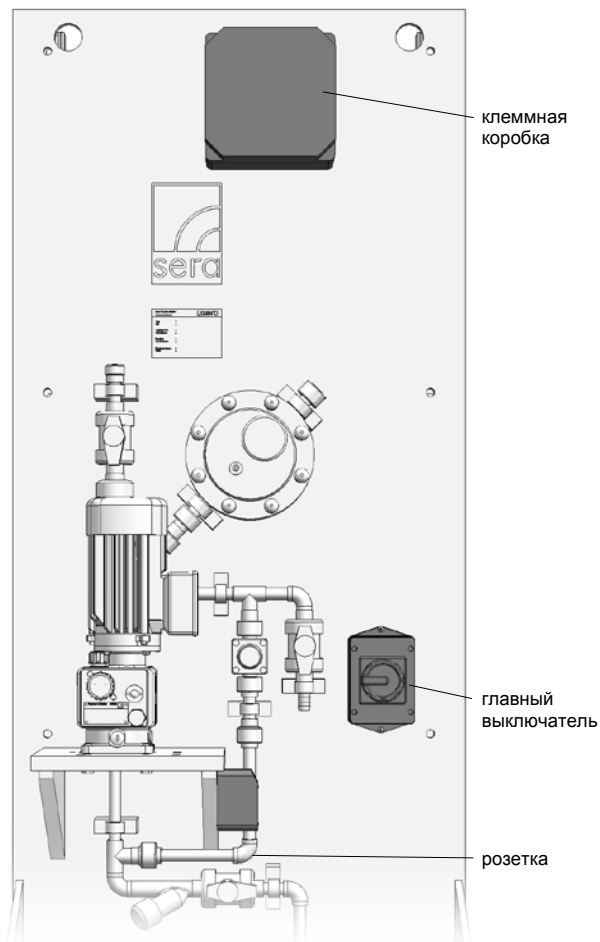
Опция клеммная коробка, розетка и главный выключатель
